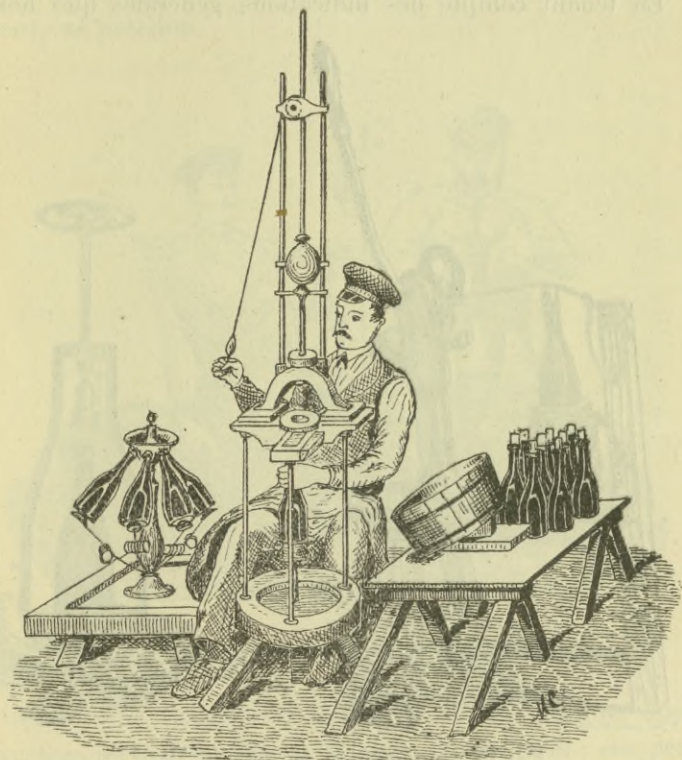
Bouchage du champagne. Machine à boucher dite mouton.
